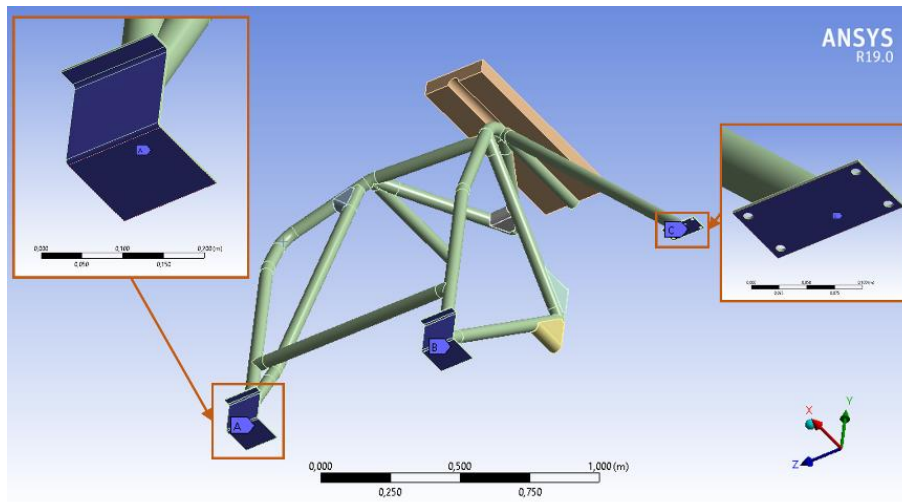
Condición tipo Fixed en las platinas de anclaje.
